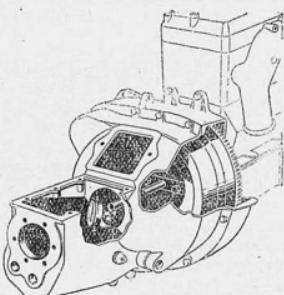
Проверка концентричности отверстия посадки подшипника первичного вала по отношению к коленчатому валу двигателя
